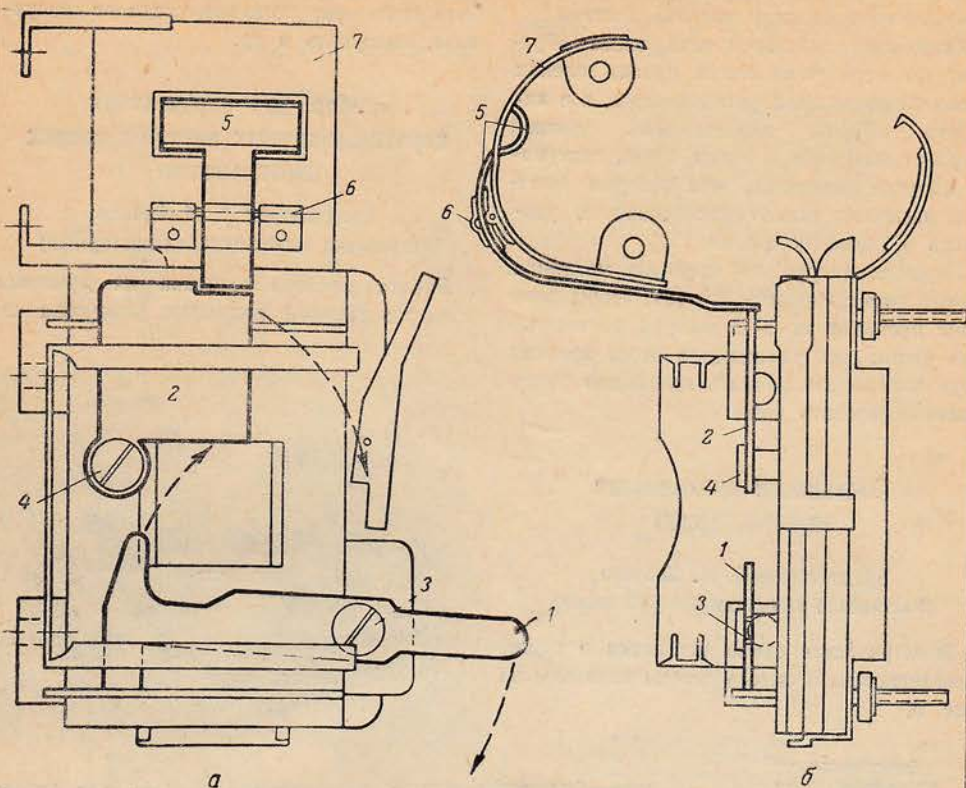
Детали автоматической заслонки и их установка на фильмовом канале
